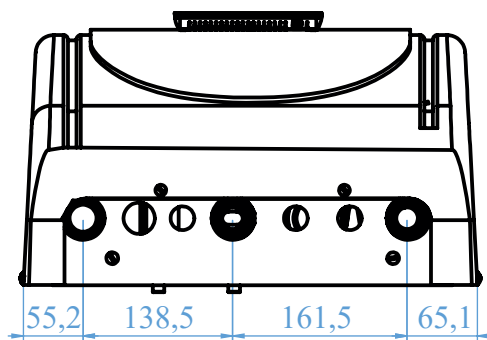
Abmessungen des Gbox-Moduls - Seitenansicht
